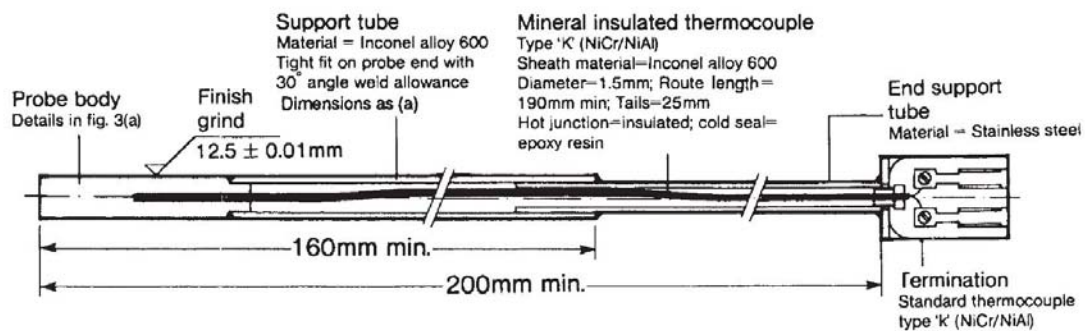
Conjunto probeta/soporte/termopar (extraído de ASTM D6482)
